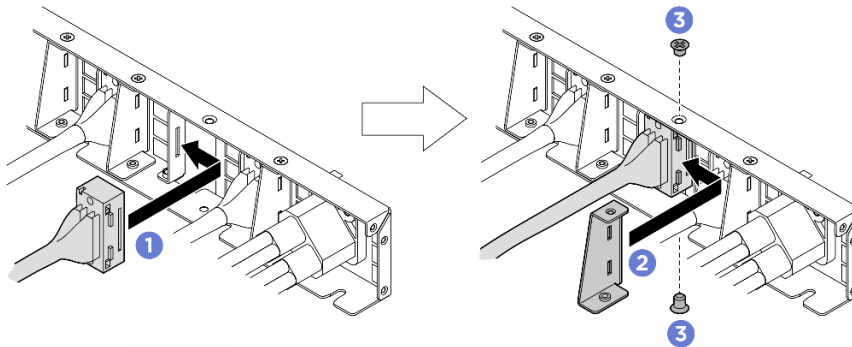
Módulo de E/S frontal, painel integrado de diagnósticos, gerenciamento de GPU ou instalação de cabo de sinal
